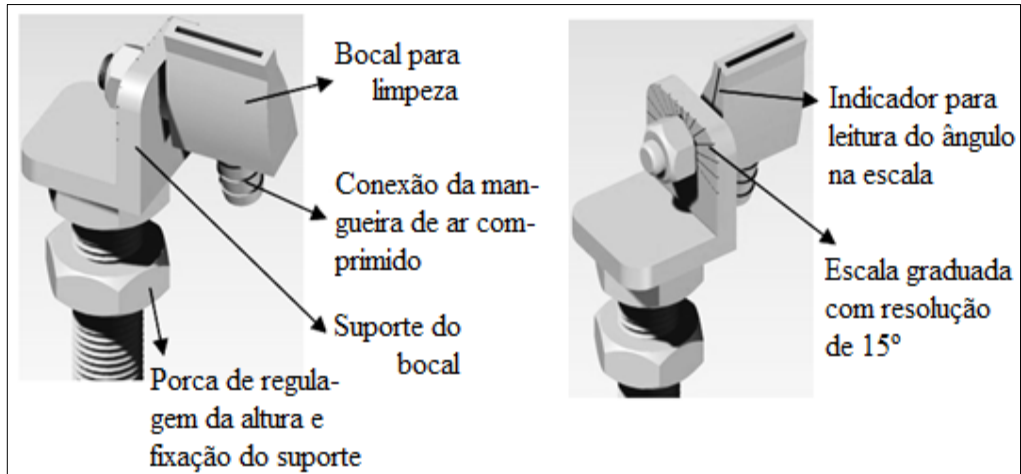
Sistema de fixação e posicionamento do bocal de limpeza
